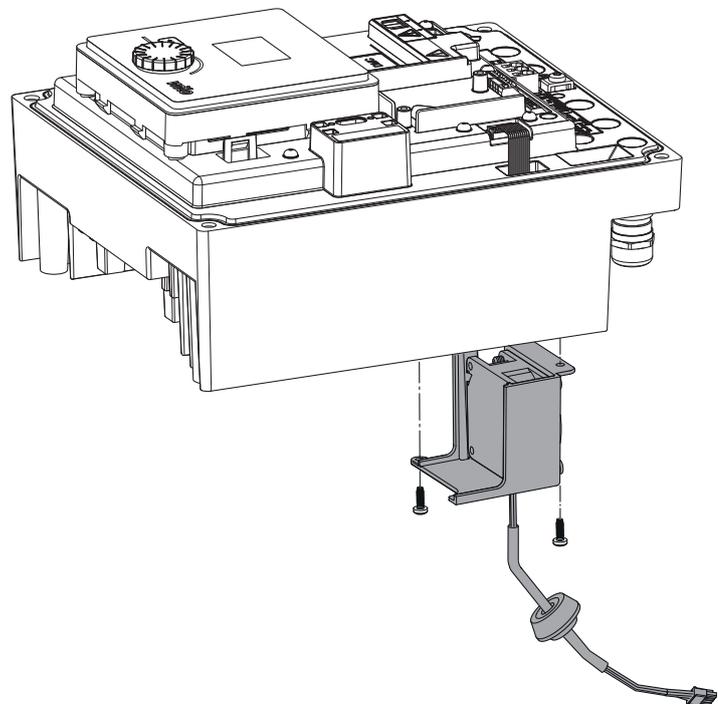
Retirar o ventilador do módulo, incluindo o cabo e o vedante de borracha
